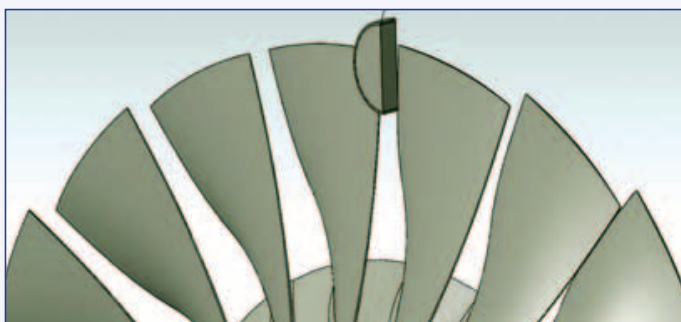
Внешний вид лопатки моноколеса с вставкой
